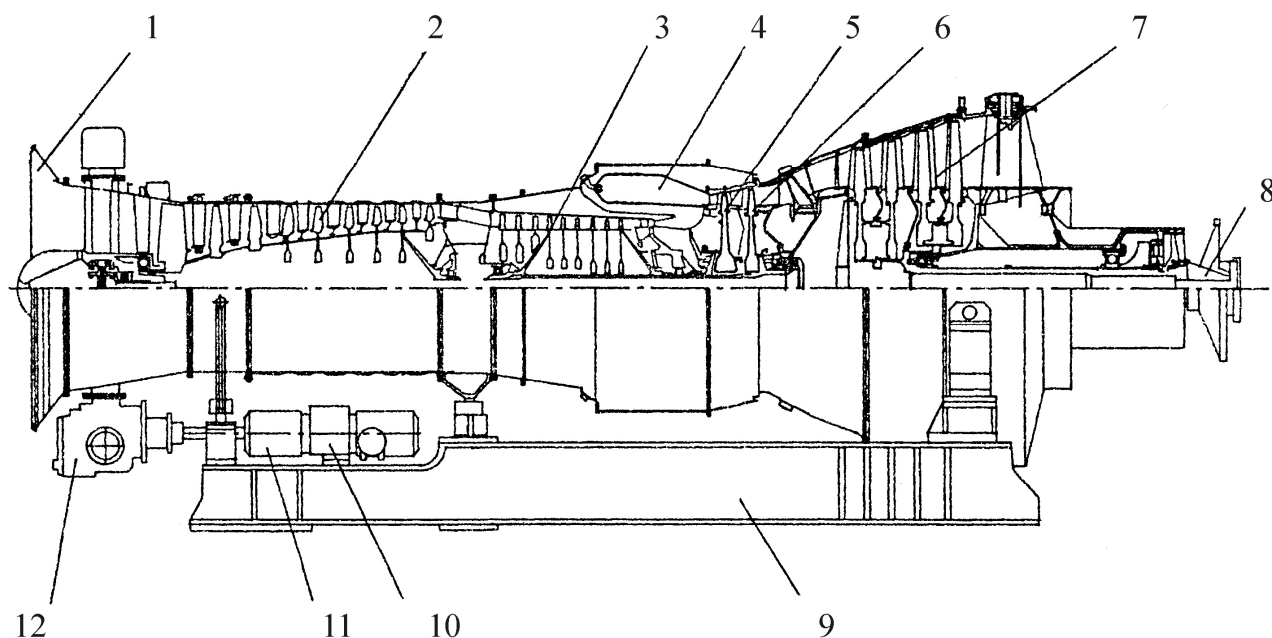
Конструктивна схема двигуна UGT 25000:
